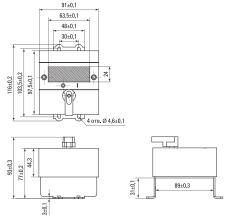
Габаритные размеры моторного привода к ВА-99М 63
